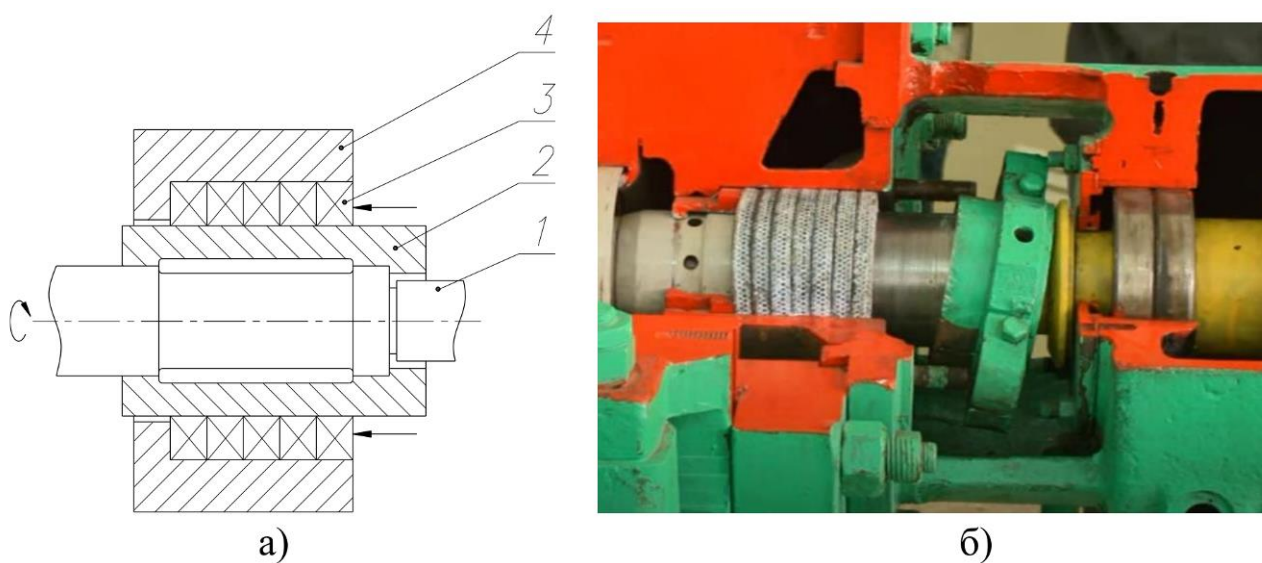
Схема роботи захисної втулки консольних насосів: а – принципова схема; б – загальний вигляд; 1 – вал; 2 – захисна втулка; 3 – сальникова набивка; 4 – корпус насоса.
